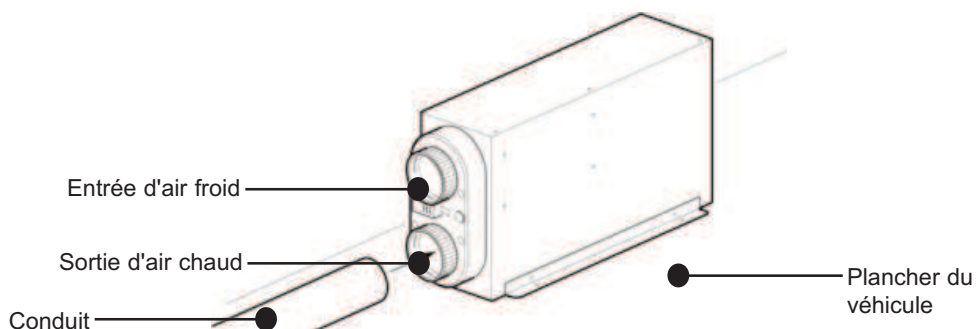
Installation interne - Raccordement au conduit d'air chaud
